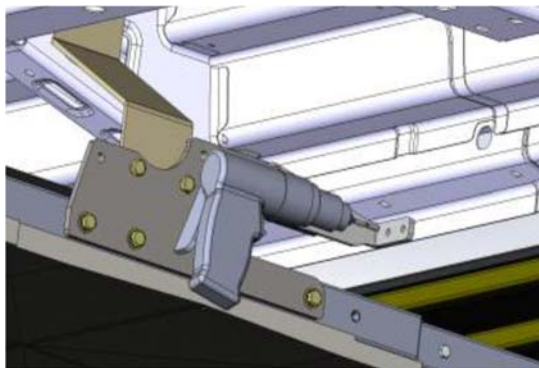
Ansicht für spätere Verschraubung werden hier am Schweller Bohrungen angebracht
